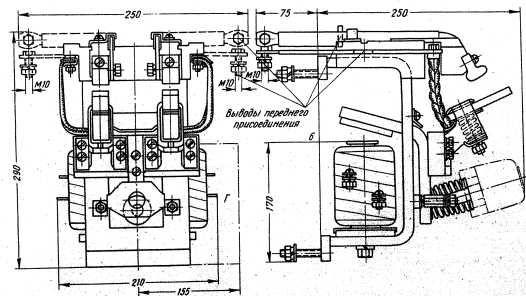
Габаритные и установочные размеры контактора с двумя НО контактами, без гашения, на номинальный ток 300 а, типа КТП 544, с задним и передним присоединением
